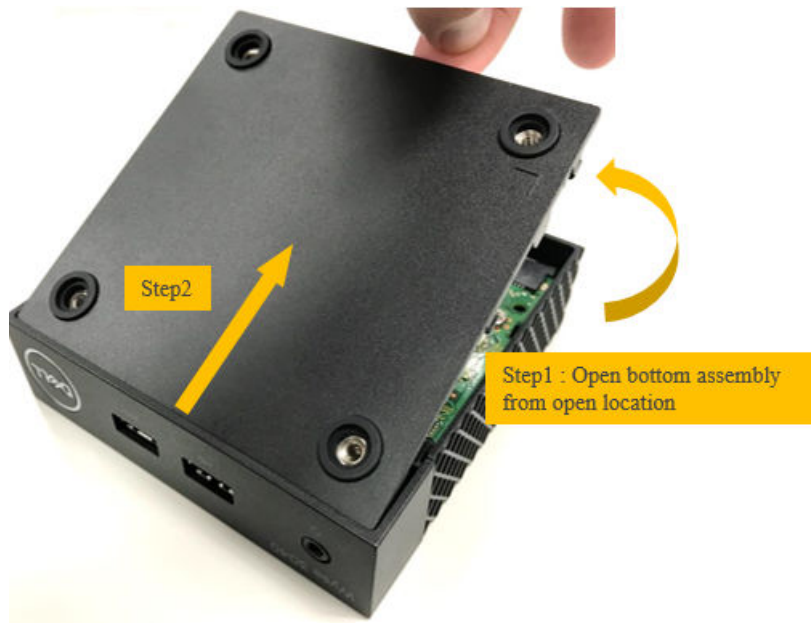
Abra el ensamblaje inferior de la ubicación abierta
